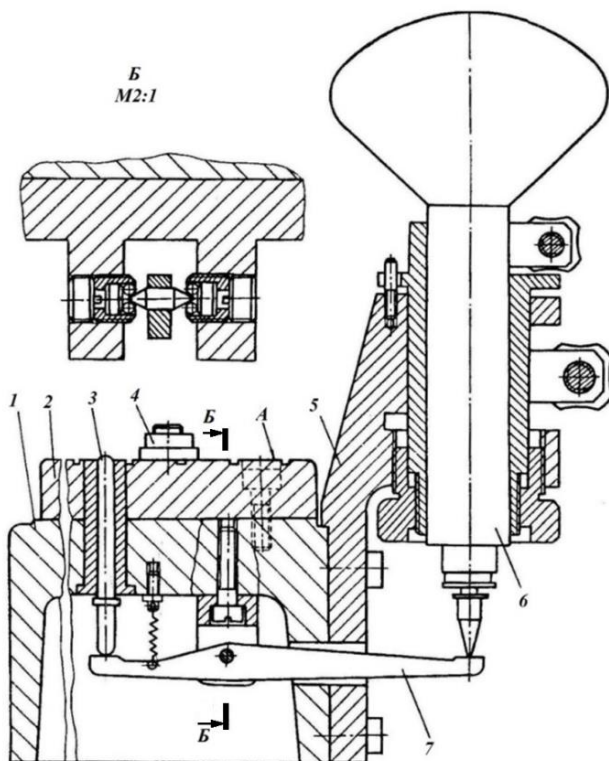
Универсальное приспособление для контроля неплоскости торцов деталей типа «кольцо»
